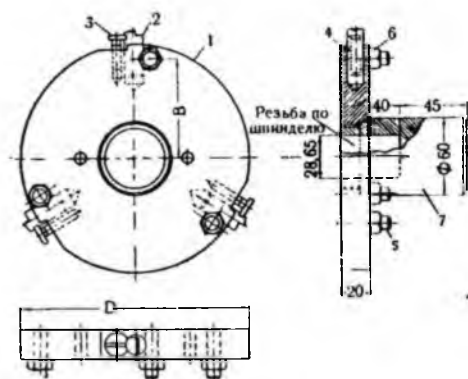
Резцовая головка расточного станка со специальной державкой для установки резцов вне станка:
